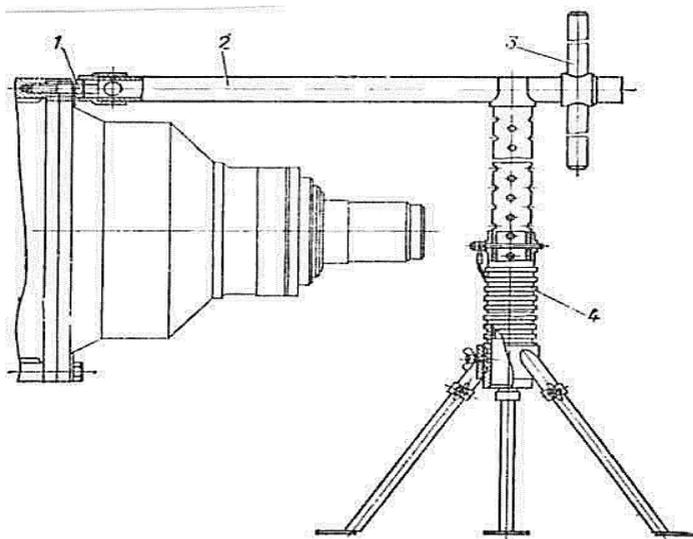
Установка ключа 175.95.023С6-1 для отвертывания болтов крепления
